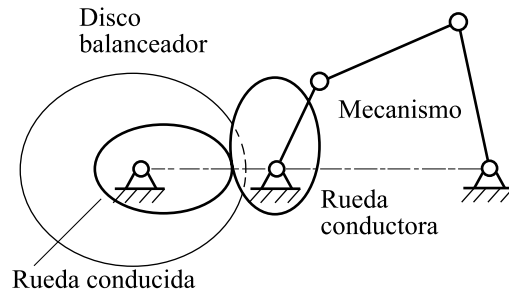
Mecanismo balanceador con engranajes no circulares. [4]
